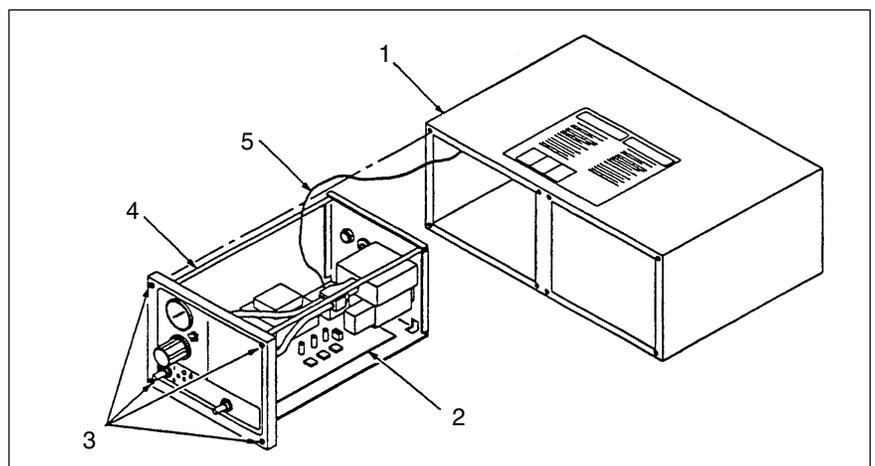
Ausbau des Steuermoduls aus dem Gehäuse
